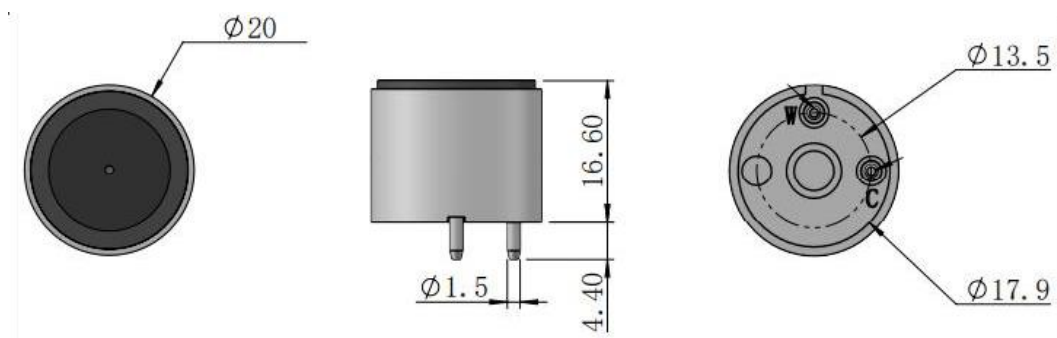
Габаритный чертеж датчика газа SSN-G2EC-CO
